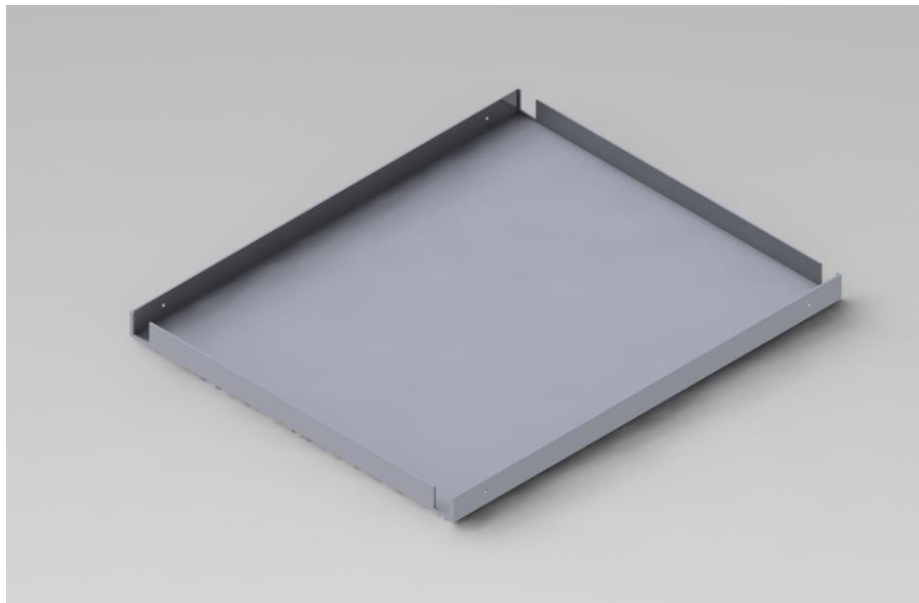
Ensamblaje subconjunto 1.3. Soldadura 6, 7 y 8.
